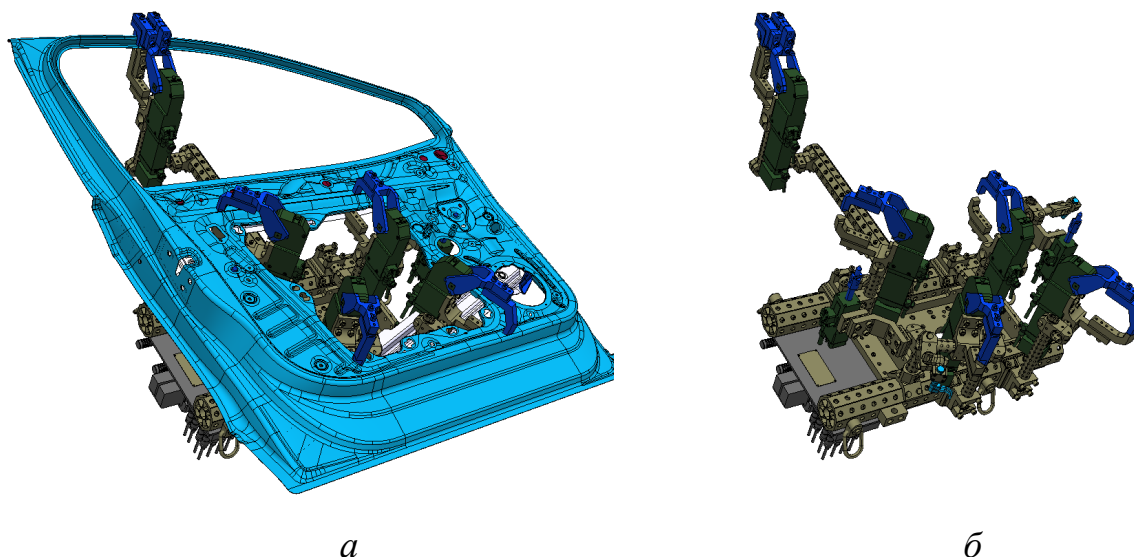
Захватное устройство для транспортировки автодетали для робота 5082R01 G
